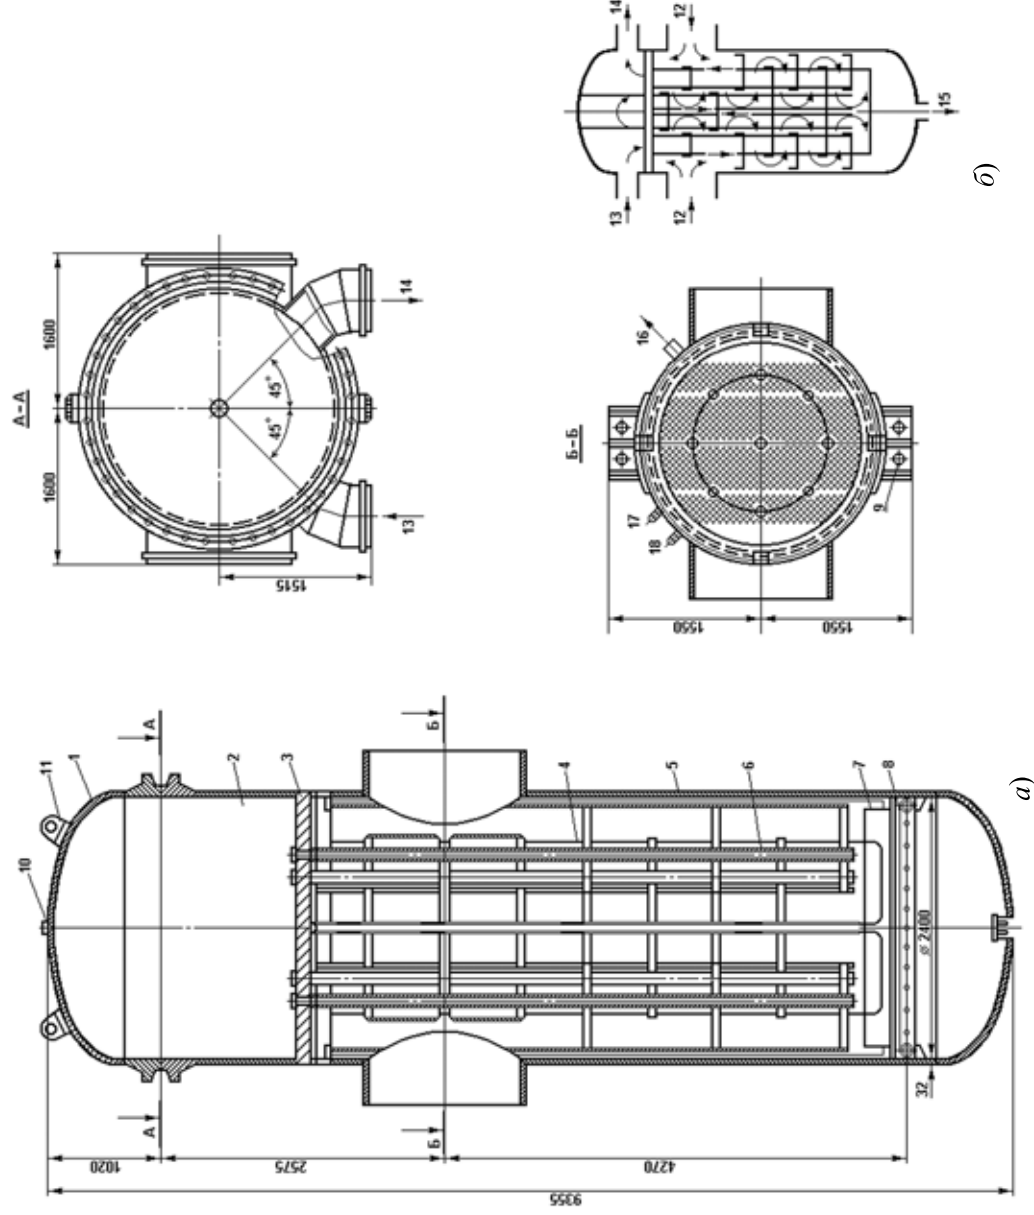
Подогреватель низкого давления ПН-1500-32-6-III: *а* – общий вид; *б* – схема движения воды и пара; 1 – крышка водяной камеры; 2 – отсеки водяной камеры; 3 – сварная трубная доска; 4 – трубная система; 5 – корпус; 6 – трубы каркаса трубной системы; 7 – гидрозатвор; 8 – кольцевое воздухоотсасывающее устройство; 9 – опорные лапы; 10 – воздушник; 11 – рымы транспортировочные; 12 – вход греющего пара; 13, 14 – вход и выход основного конденсата; 15 – выход конденсата греющего пара; 16 – отвод воздуха; 17 – указатель уровня; 18 – коллектор для присоединения импульса регулятора уровня
